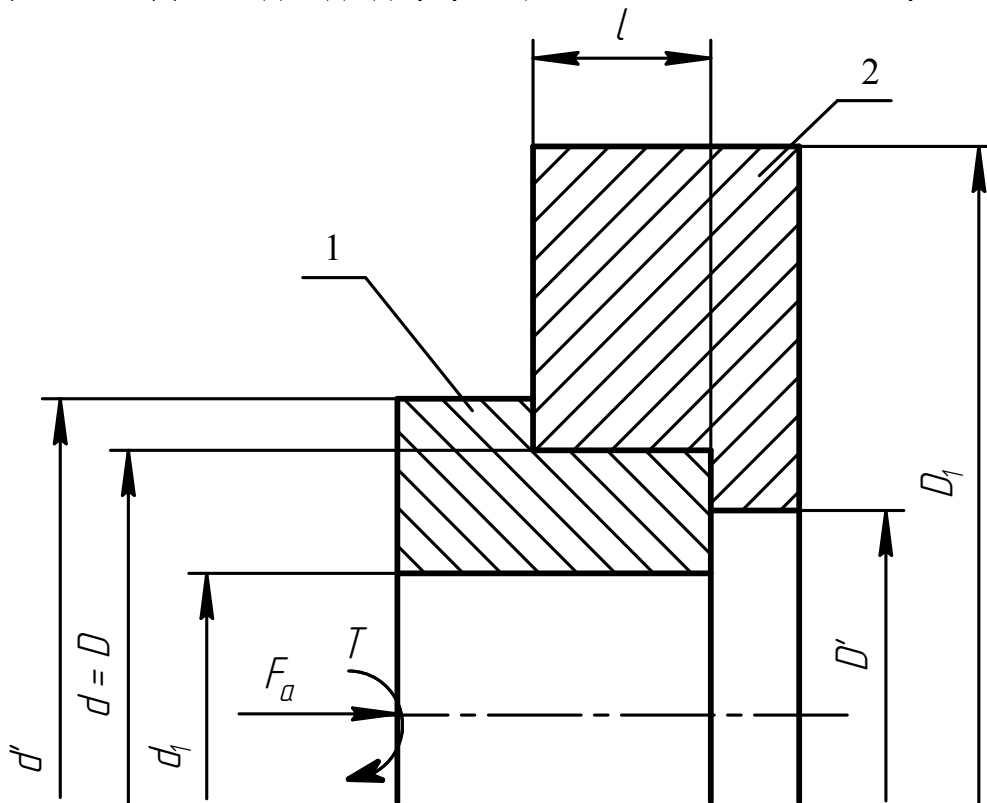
Розрахункова схема з'єднання з натягом
